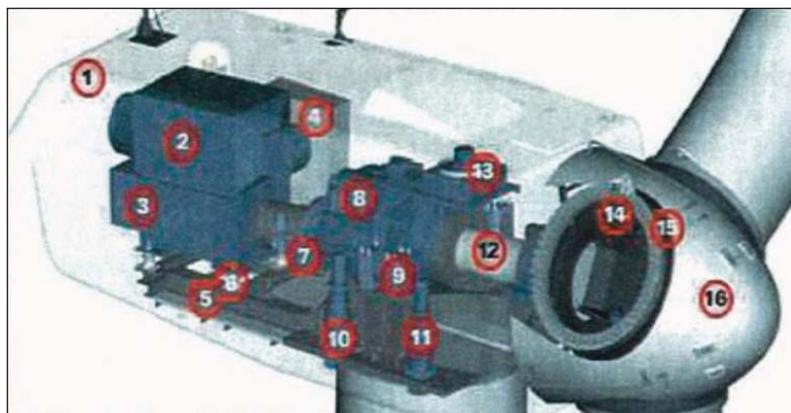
Основные компоненты гондолы: 1 — гондола; 2 — теплообменник; 3 — генератор; 4 — контрольный щит; 5 — главная рама; 6 и 9 — противозумная изоляция; 7 — гидравлический стояночный тормоз; 8 — редуктор; 10 и 11 — система поворота гондолы; 12 — вал ротора; 13 — охладитель смазки; 14 — управление шагом лопасти; 15 — ступица ротора; 16 — конус передней части
